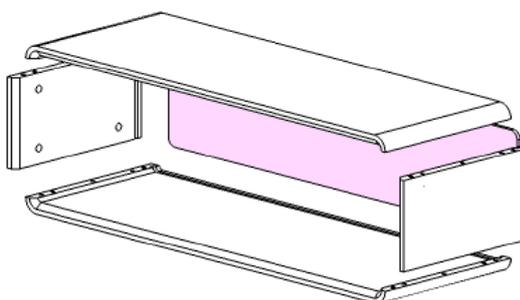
Parte superior do móvel em vista isométrica com vista explodida.
